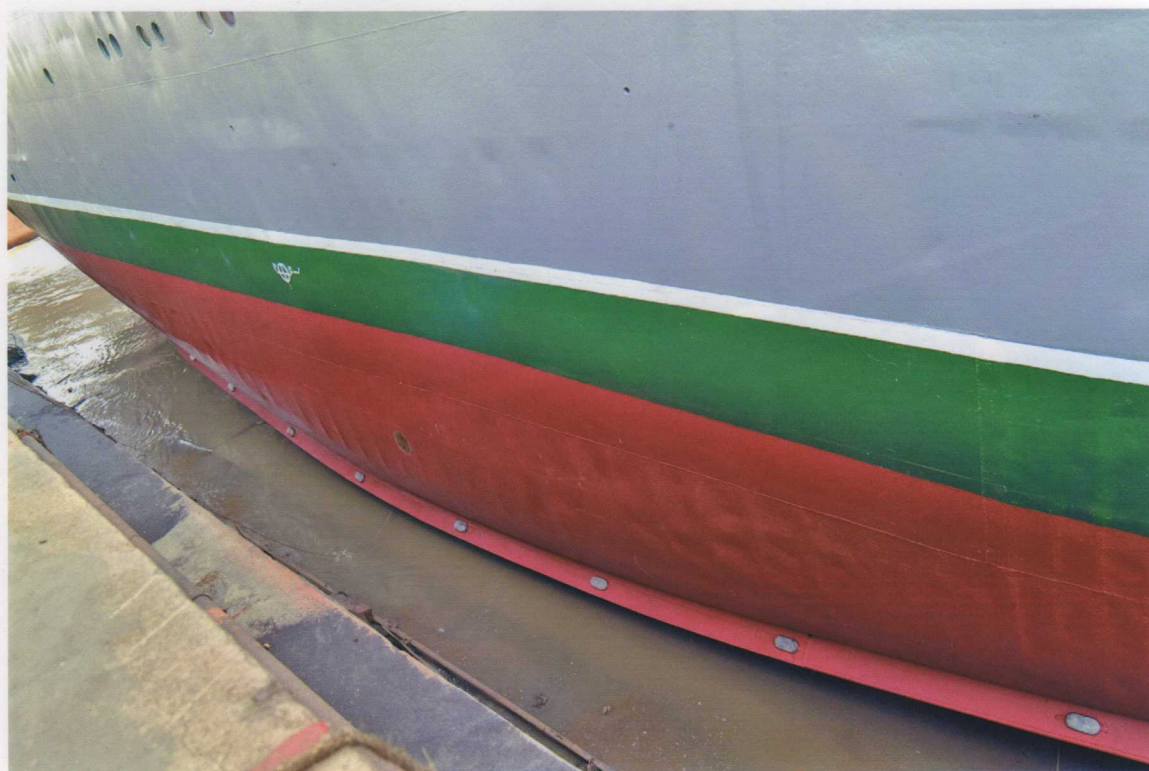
Пояс переменных ватерлиний ПБ корпуса судна
